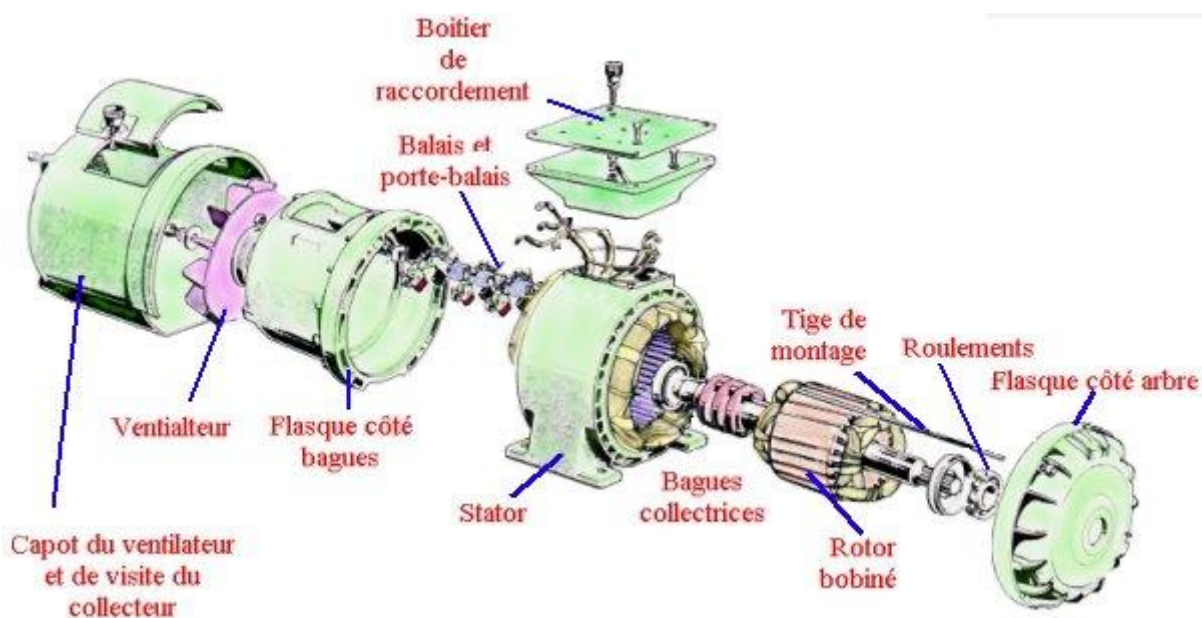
Description de différentes pièces d'un moteur asynchrone triphasé à rotor bobiné (à bagues).
